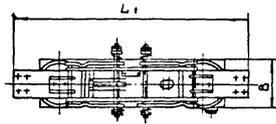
Разъединитель трехполюсный типоразмера РВ 10/400-630-1000 УХЛ2, РВ 11/630-1000 Т2
